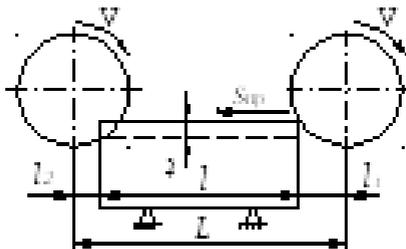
Схема обработки цилиндрической фрезой
